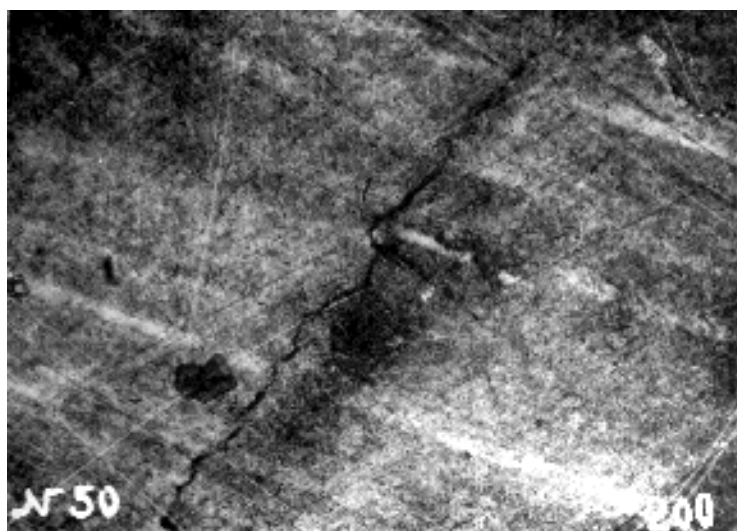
Трещина в металле шестерни, ×200
